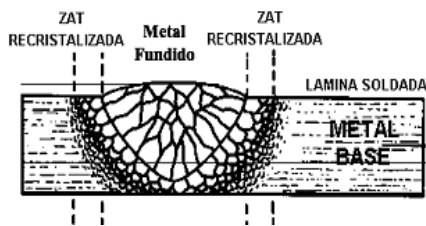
Esquema de las zonas involucradas en un cordón de soldadura.
